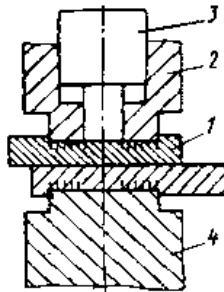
Схема точечной сварки с односторонним деформированием свариваемых деталей.
